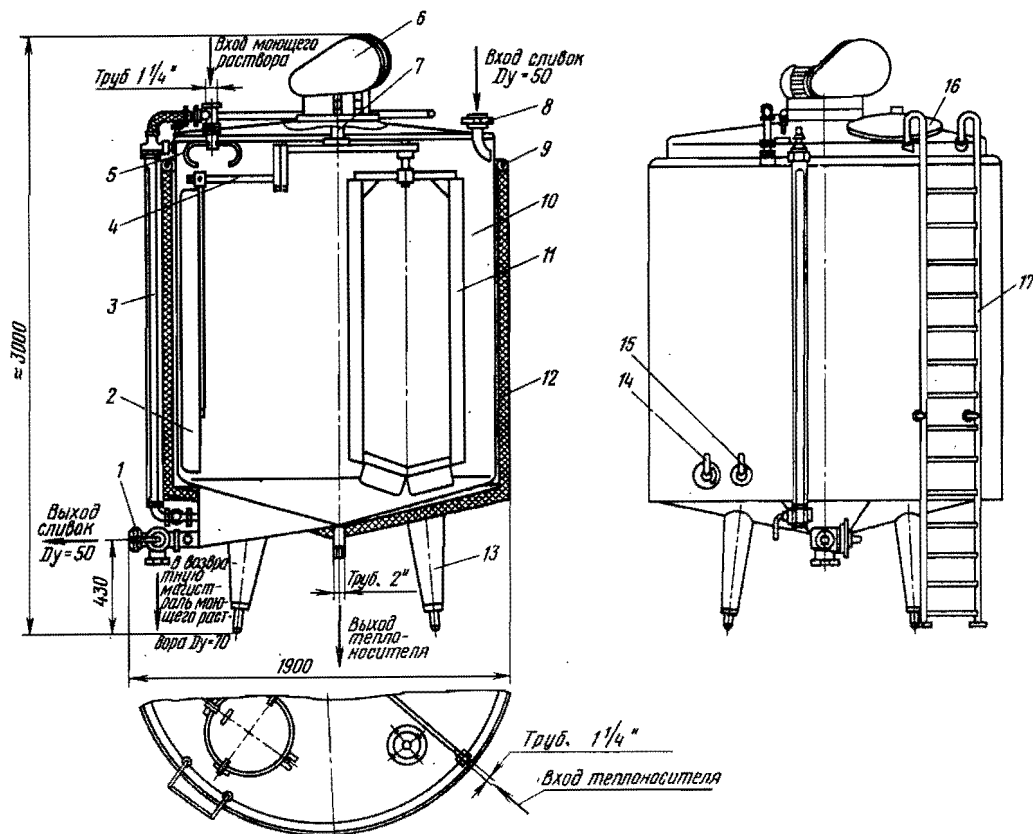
Общий вид резервуара сливоксозревательного марки РЗ-ОТН-3000:
